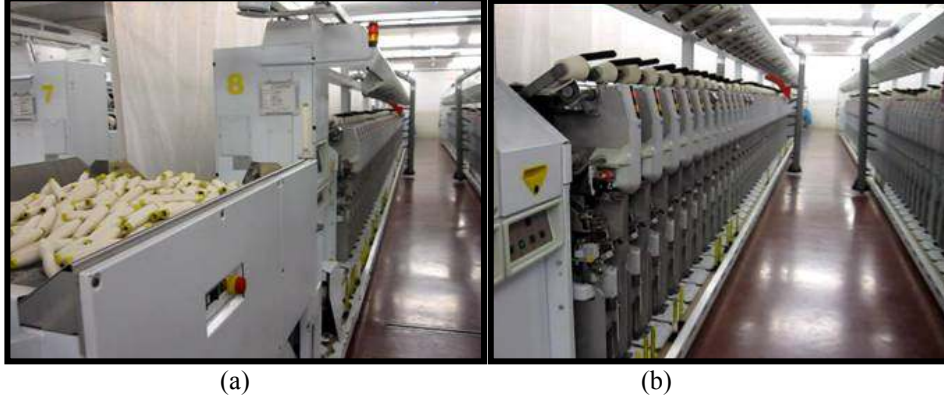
(a) Zinser FL 670 Fitol Makinesi, (b) Rieter G33 Ring iplik makinesi.
